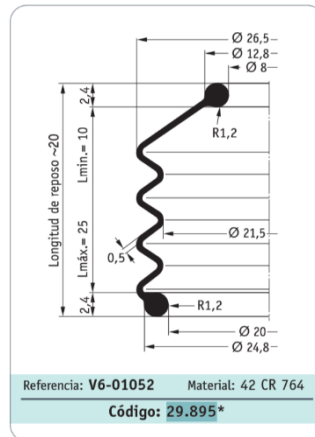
Dimensiones del fuelle Prot. 1 [12]
